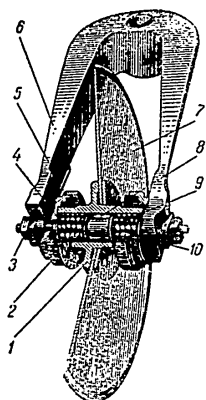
Нож дисковый. 1 — ступица; 2 — колпак; 3 — втулка; 4 — кольцо регулировочное; 5 — манжета резиновая; 6 — вилка; 7 — диск ножа; 8 — втулка распорная; 9 — роликоподшипник; 10 — ось диска
